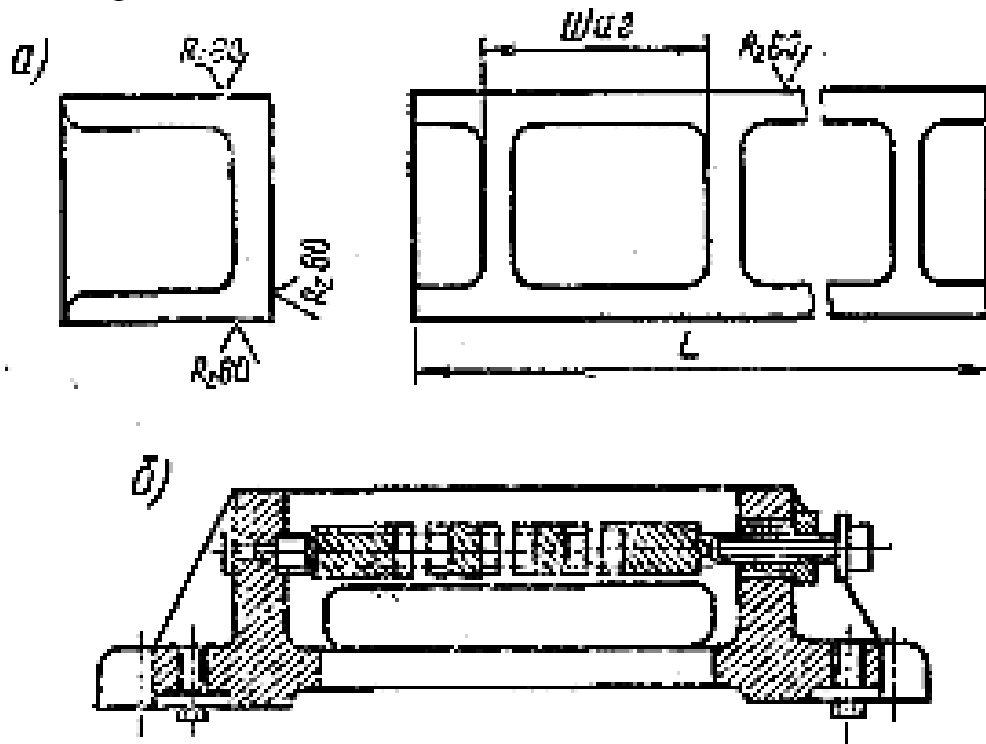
Заготовка корпусу пристрою із швелера (а) і його використання (б)
